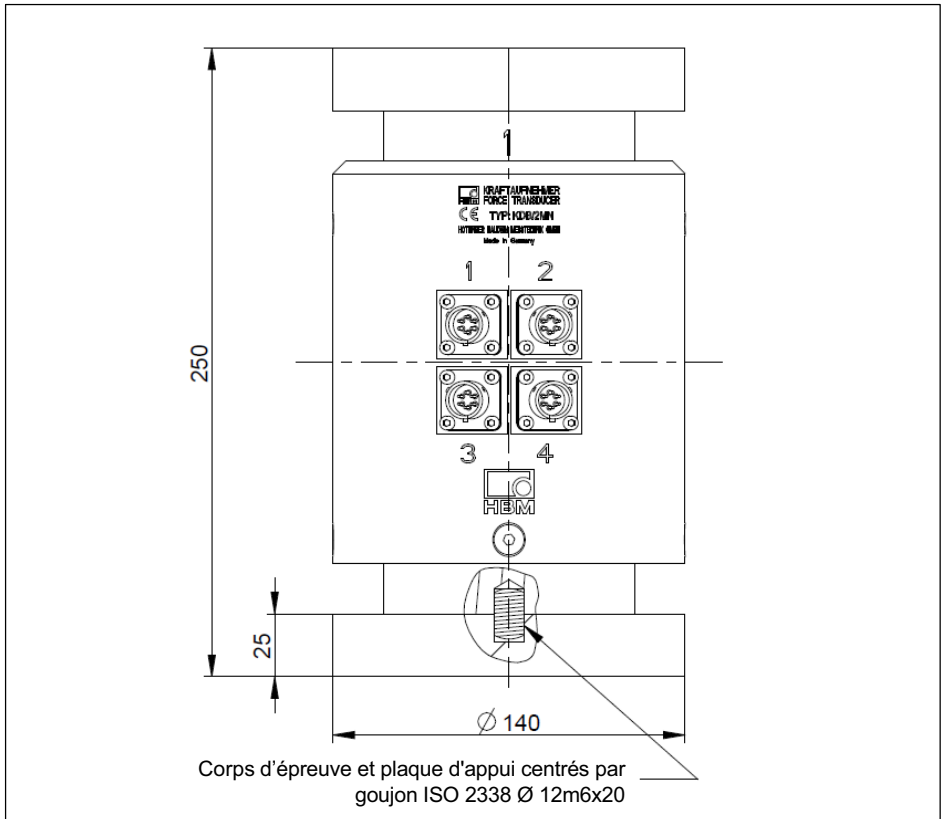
Dimensions du dispositif de mesure de force avec plaques trempées montées (à utiliser pour contrôler des machines d'essai de matériaux de construction)
